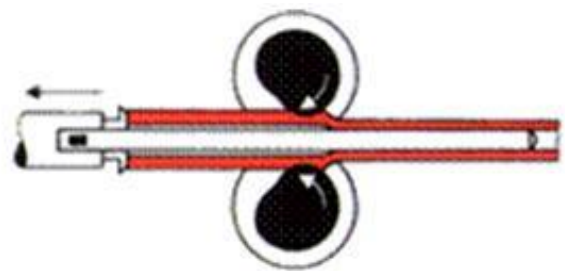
схема холодної пільгерної прокатки труб (ХПТ)
